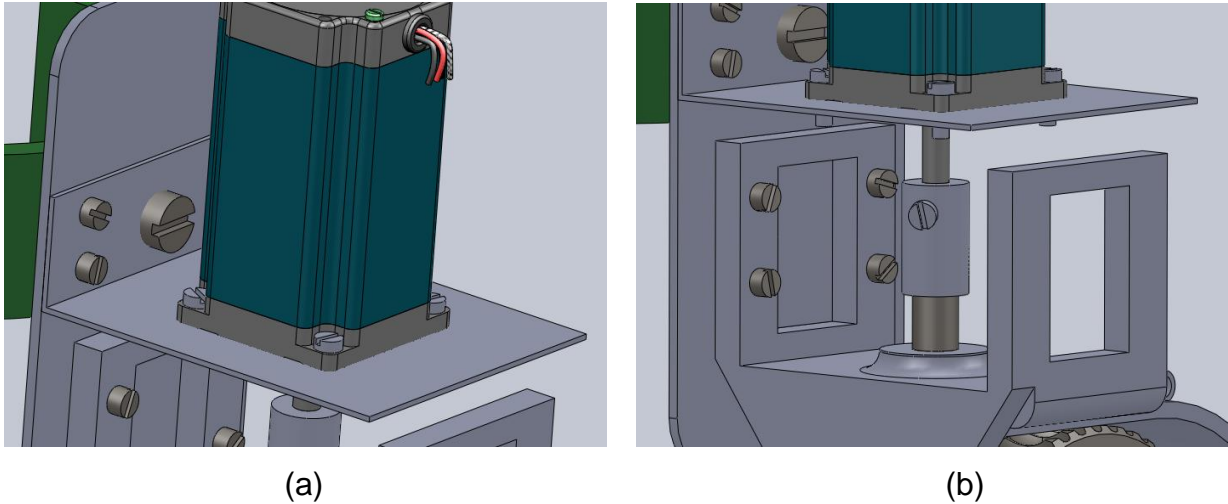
(a) Fixação do motor de passo e (b) acoplamento entre eixo do motor e eixo da caixa de redução.
